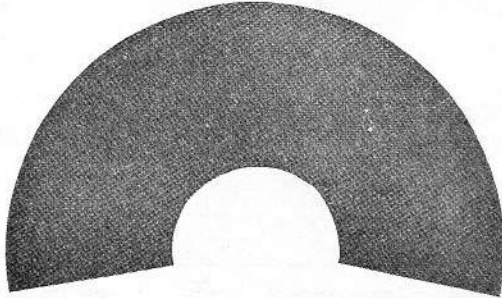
Schmiederisse in einer Kolbenstange.
